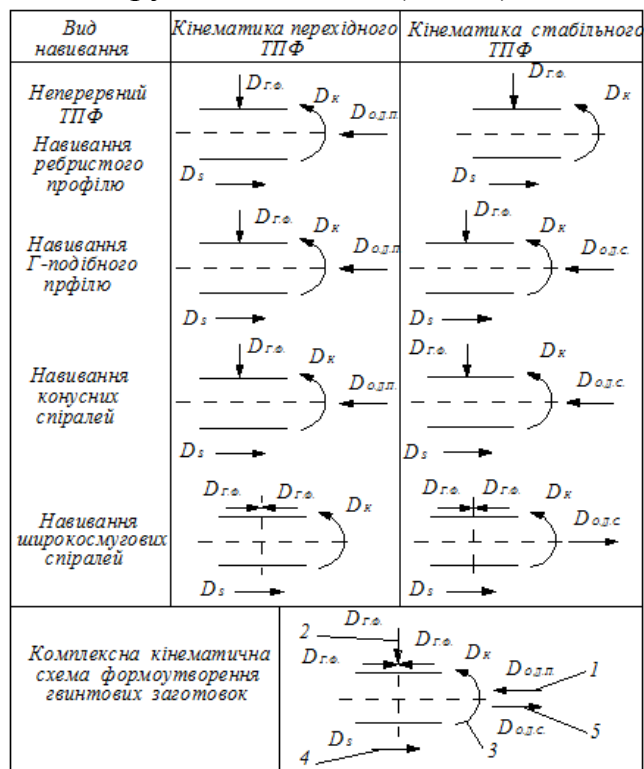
Кінематика формоутворення гвинтових заготовок
